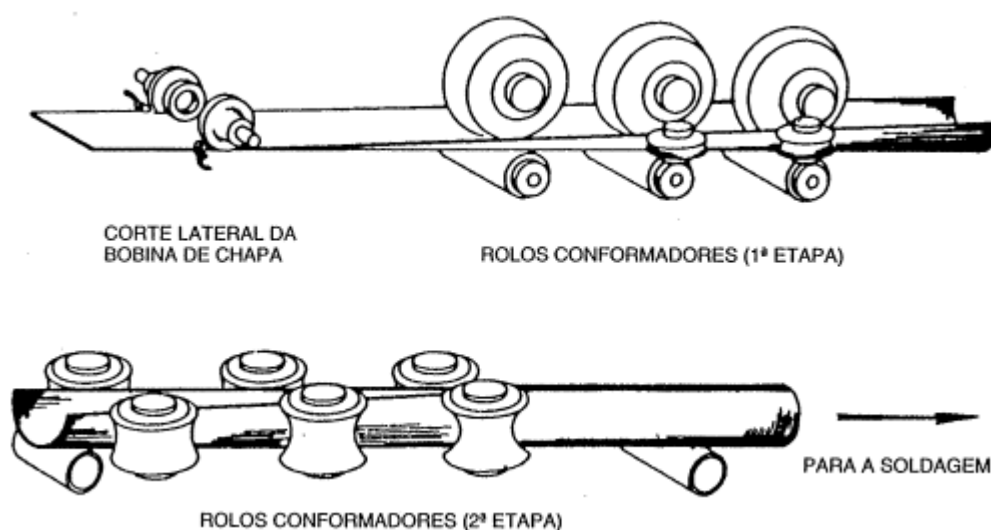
Fabricação de tubos a partir de bobinas de chapa
